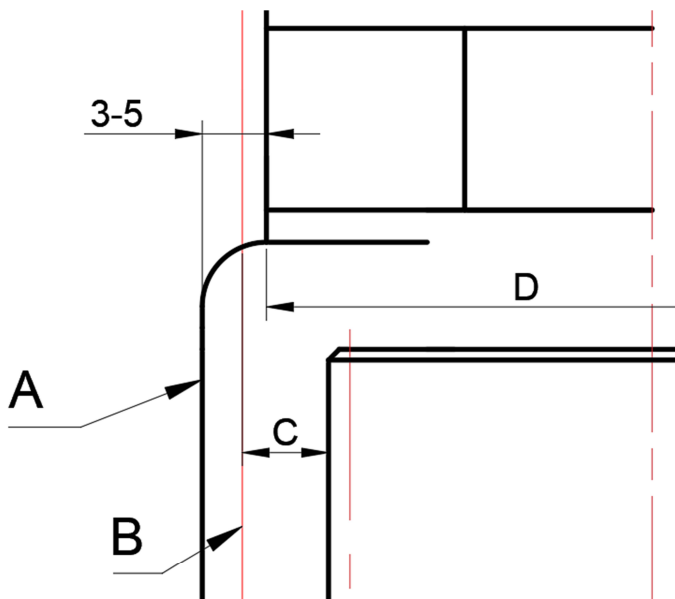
Изображение внутренней поверхности стенки редуктора
